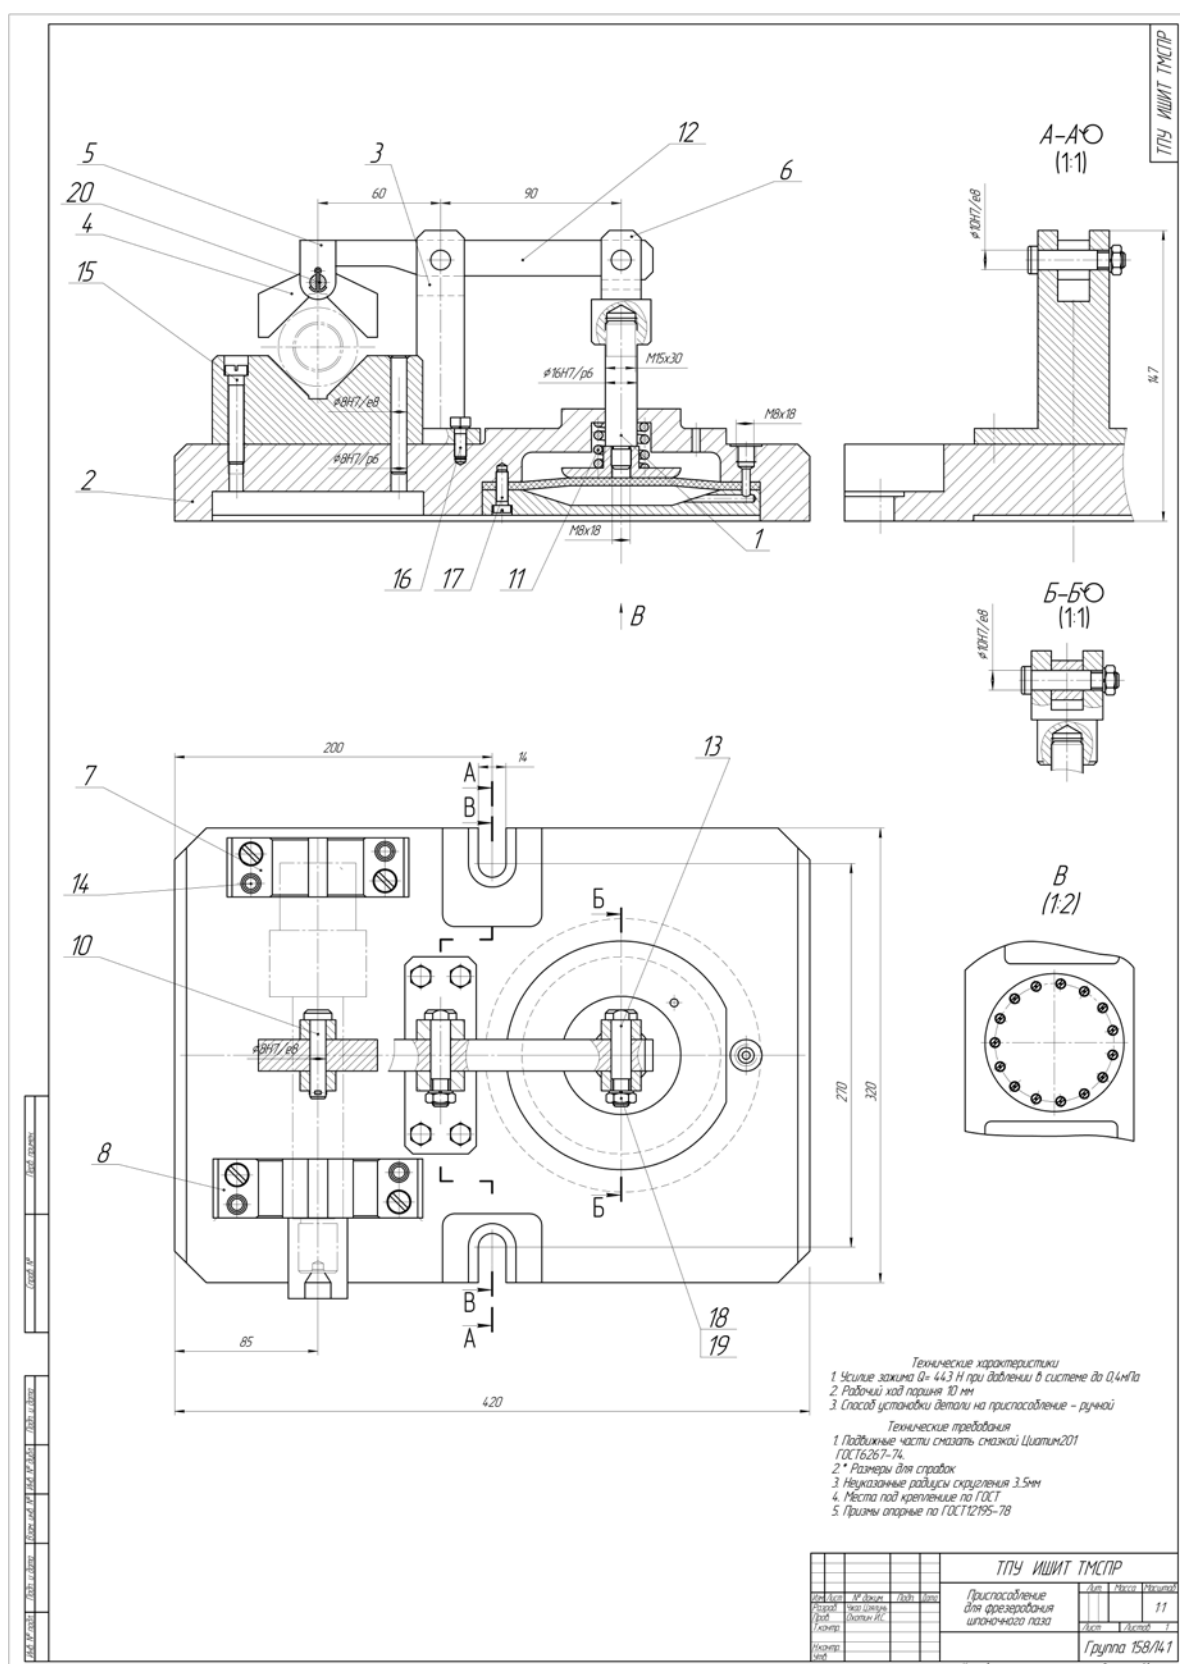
Сборочный чертеж приспособления приведен на формате А1
